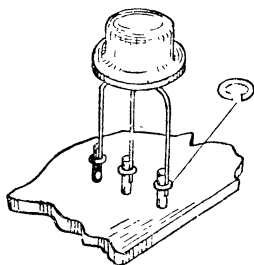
Способ крепления выводов деталей на опорных шпильках.
